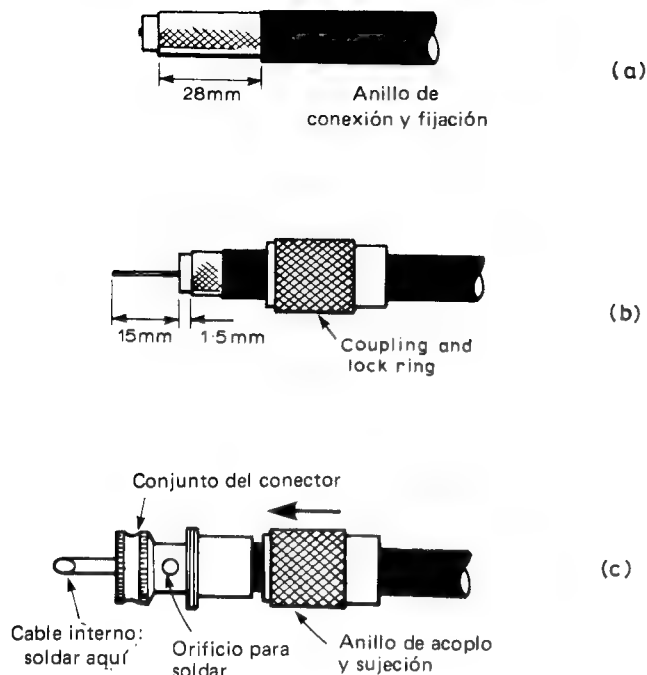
(a) Cable pelado y listo para la operación (b). (b) Conductor interior preparado y anillo de sujeción puesto. (c) Conjunto del conector ya puesto y soldado como se indica.
